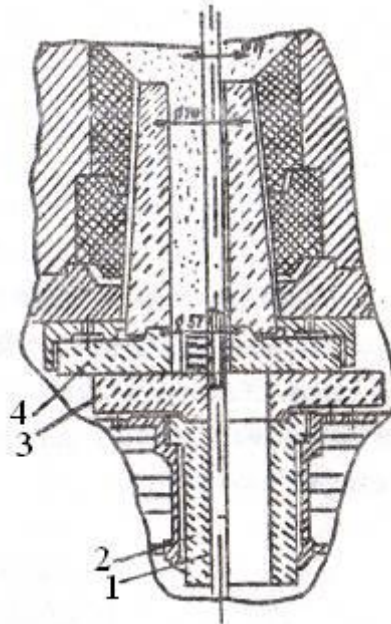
Схема побудови шиберного затвора, що може використовуватися для продувки сталі нейтральним газом: 1 – продувна пола штанга; 2 – сталерозливний стакан; 3 і 4 – рухома і нерухома плита
